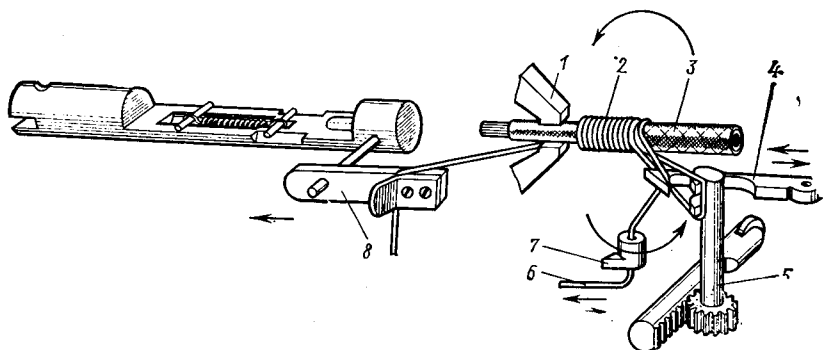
Схема полуавтомата для наложения ниточного бандаж
